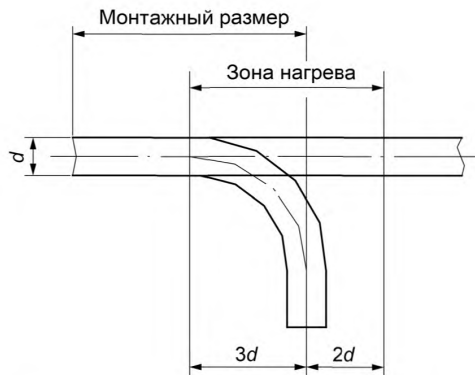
Зона нагрева трубы для выполнения гибки под углом 90°
